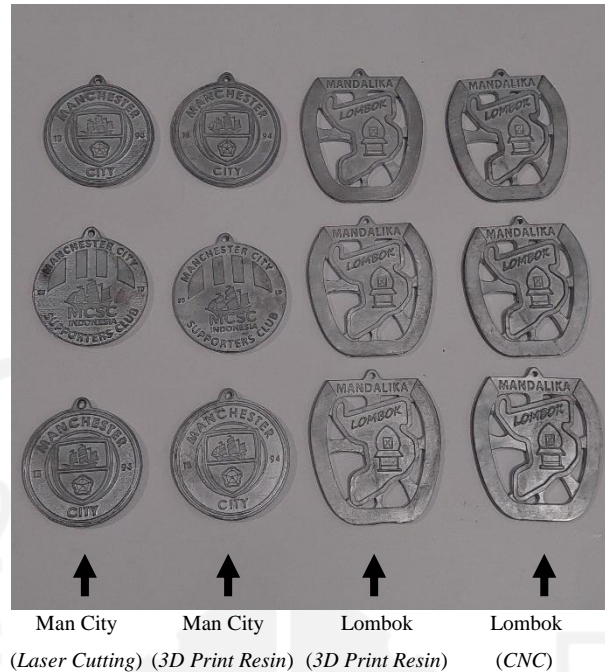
19 Hasil *Spin Casting* (CW, 750 rpm)
